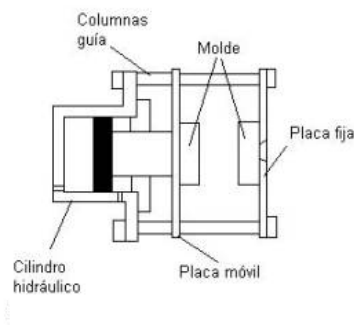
Sistema de cierre y apertura de molde de inyección de plástico
